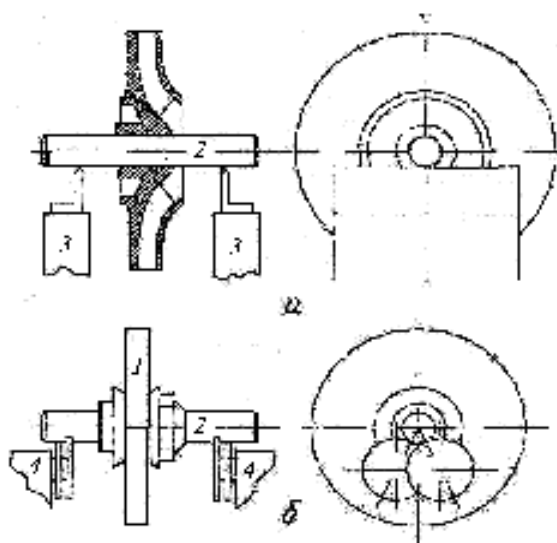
Схемы статической балансировки рабочих колес насосов: а - на параллельных призмах; б - на роликах; 1 - балансируемое колесо; 2 - вал; 3 - призмы; 4 – ролики
